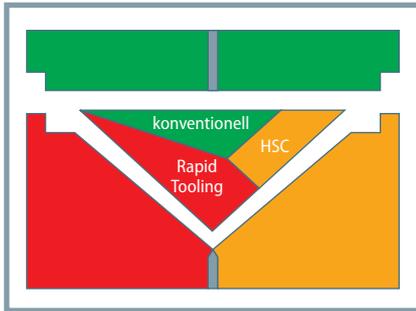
Bestandteile des Hybrid Molding sind neben dem konventionellen Werkzeugbau additiv gefertigte Formeinsätze und HSC-Fräsen Quelle: Eisenhuth; © Grafik: Hanser
